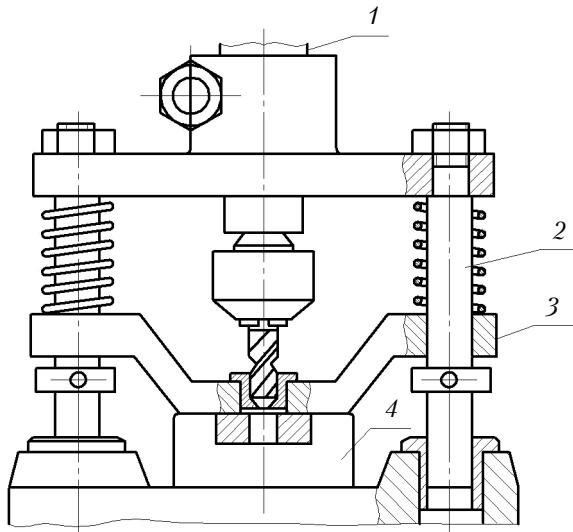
Схема автоматизированного пружинного зажима заготовки в сверлильном приспособлении
